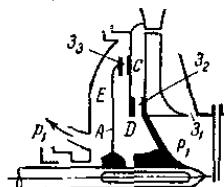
Схема разгрузочного устройства с помощью гидравлической пяты.
